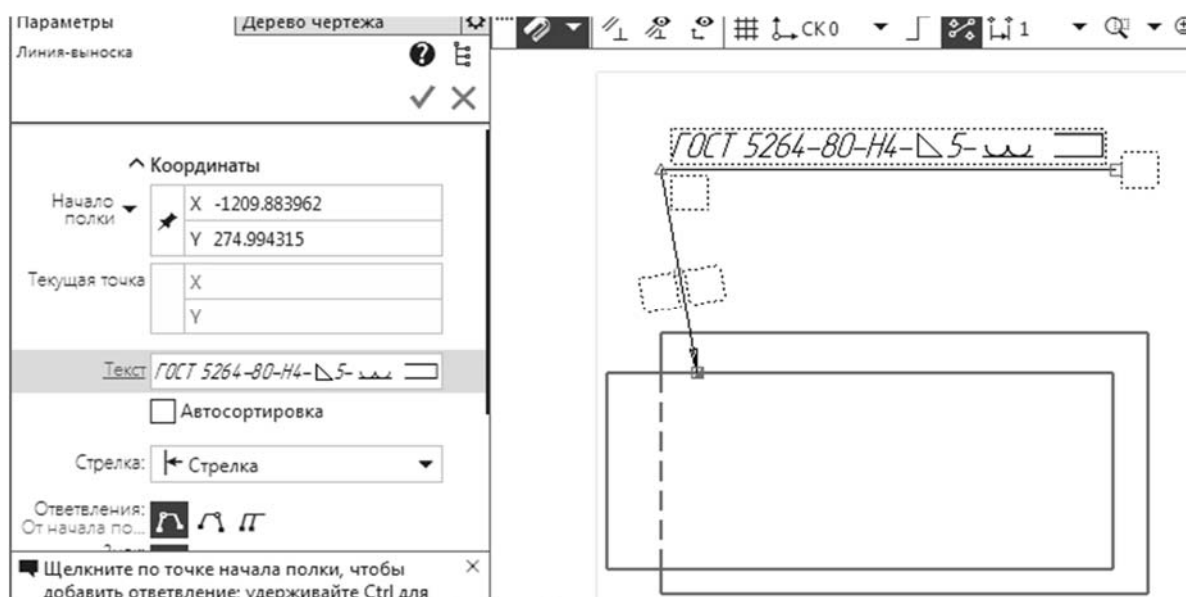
Заполнение условного обозначения сварного шва
